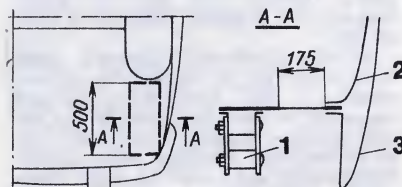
Разметка окна в багажном отсеке (слева вид сверху): 1 — рессора; 2 — усилитель крыла; 3 — крыло.
